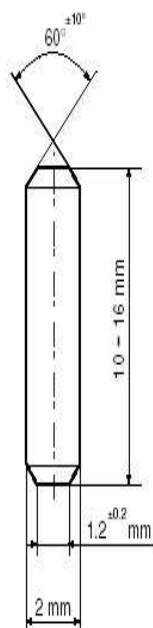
Géométrie de l'éprouvette de dilatométrie
